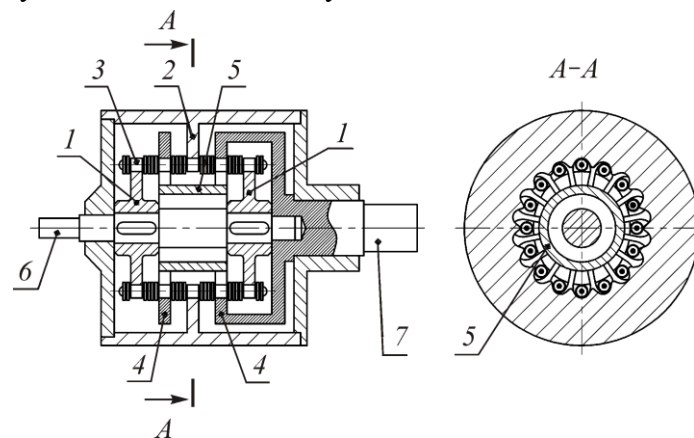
Волновая цепная передача: 1 — двухкулачковый генератор волн; 2 — жесткое колесо; 3 — пятирядная втулочная цепь; 4 — двухвенцовая звездочка; 5 — втулка; 6, 7 — входной; выходной вал соответственно
